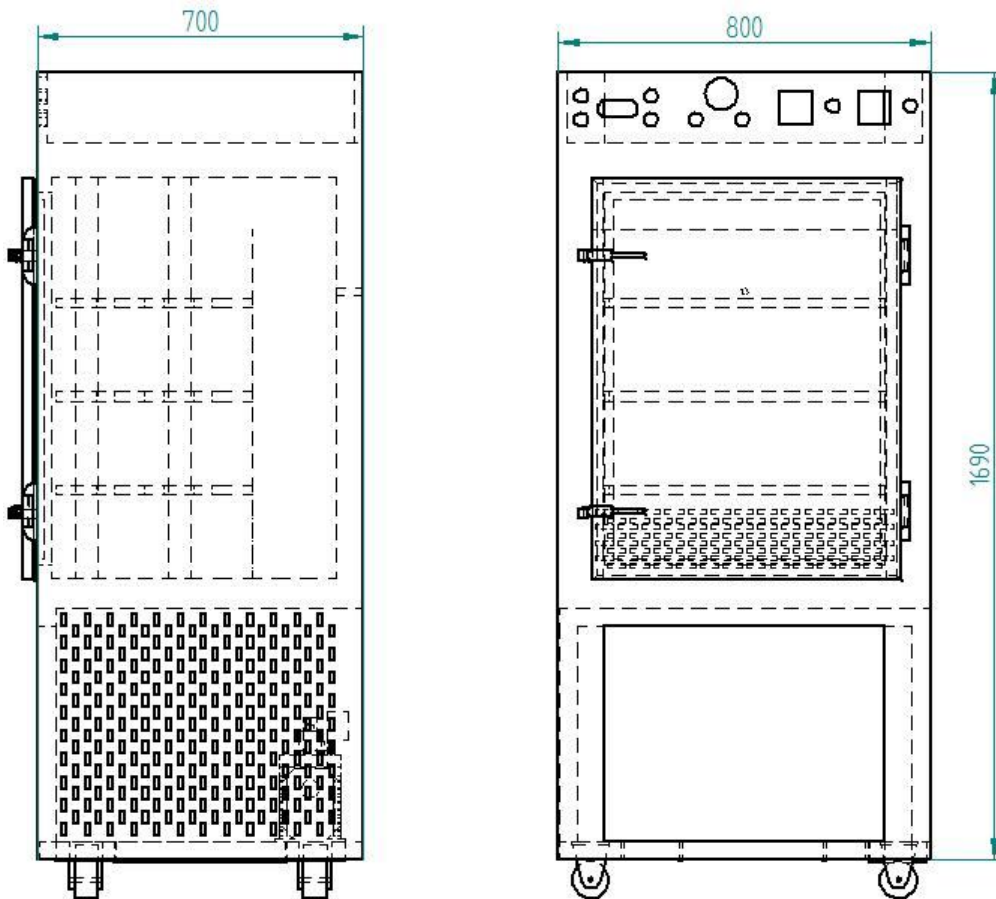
Vista frontal y lateral de la estructura del liofilizador piloto.
